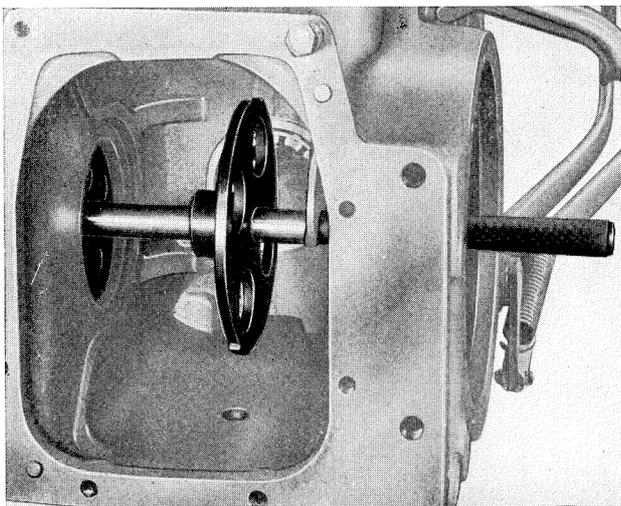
Vue arrière de l'outil A 137010 pour le réglage du couple conique.
